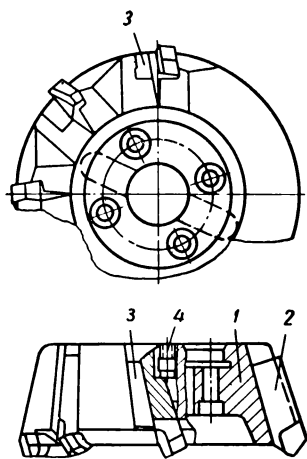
Крепление ножей гладким клином в корпусе торцовой фрезы (конструкция завода «Фрезер»):
